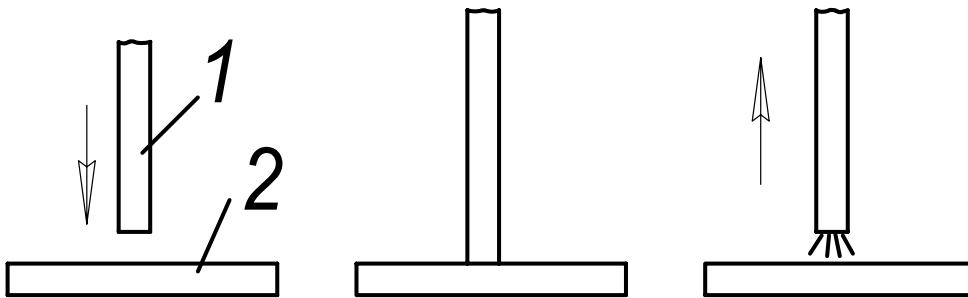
Схема зажигания сварочной дуги:
